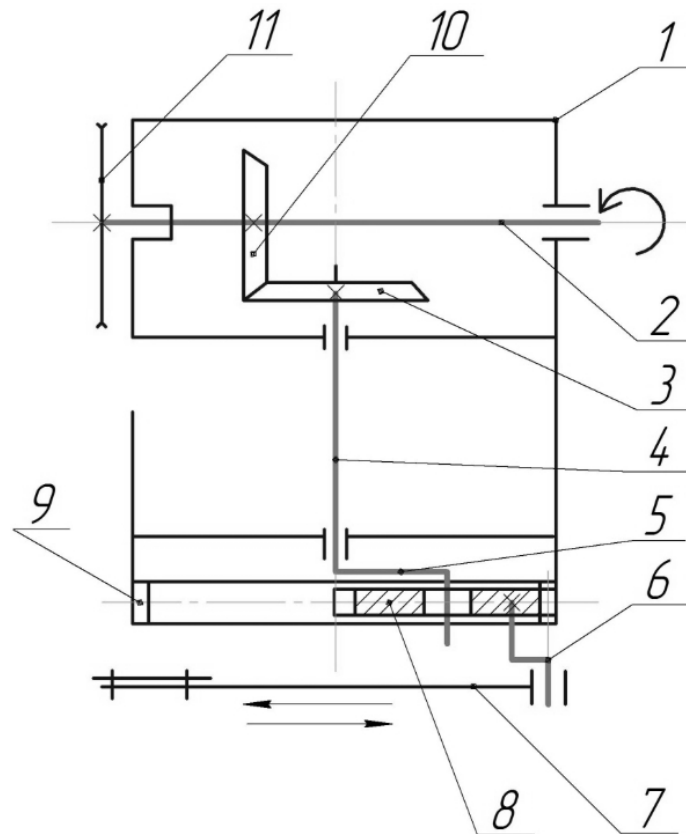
Привід ножа планетарного типу: 1 – корпус; 2 – вал ведучий; 3, 10 – конічна передача; 4 – вал ведений; 5 – водій; 6 – цапфа; 7 – ніж; 8 – сателіт; 9 – шестерня корончата; 11 – шків приводний
